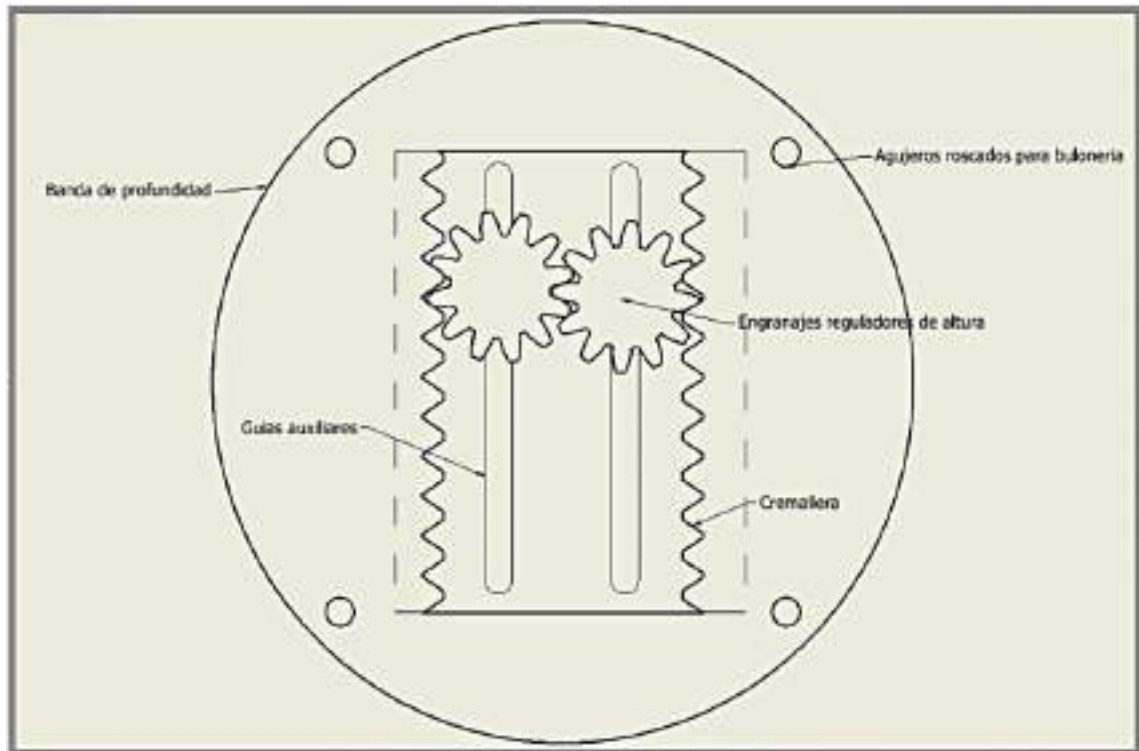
Conjunto cremallera y engranajes reguladores de altura. Fuente: elaboración propia.
